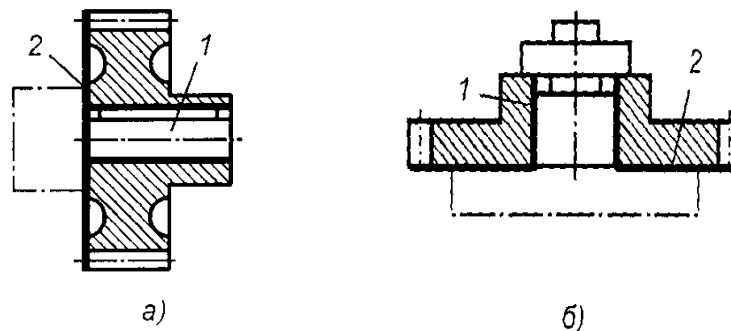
Схема основных конструкторских и технологических баз зубчатых колес
